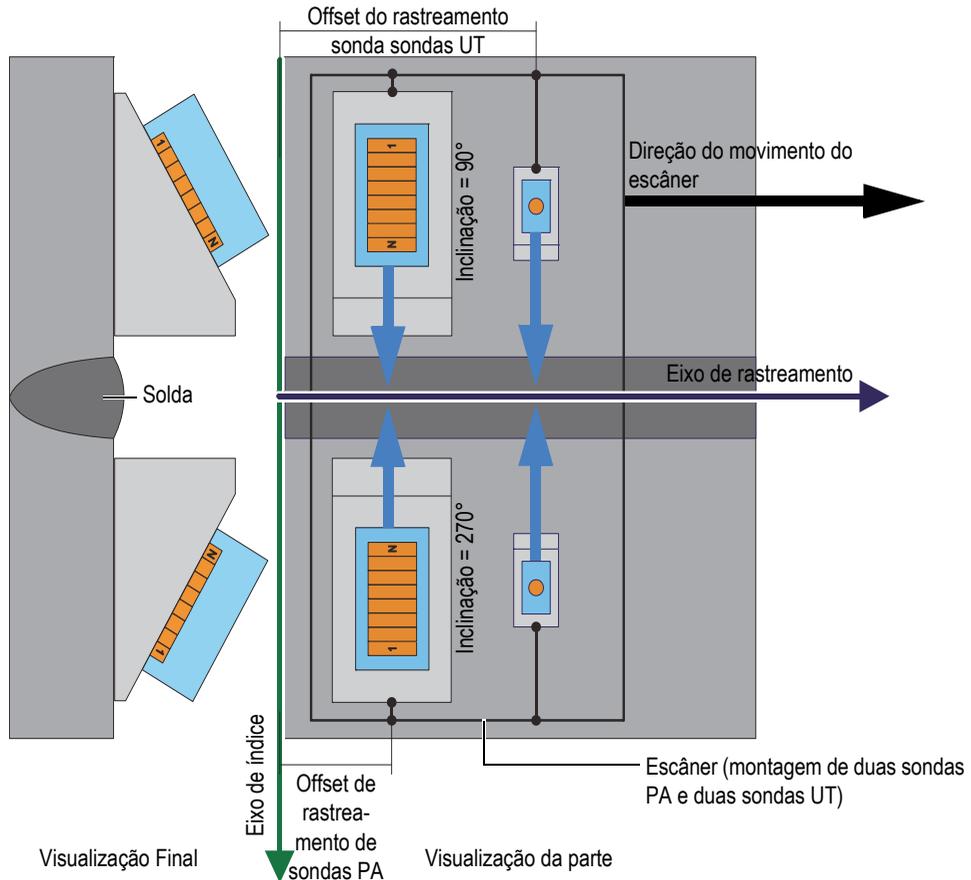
Inspeção de solda usando um escâner com sonda com inclinação de 90° e 270°
